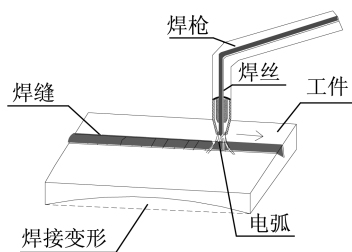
车体侧墙连接板对接焊的焊接示意图
